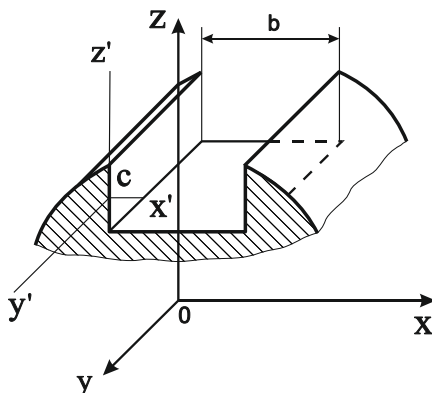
Координаты боковой поверхности шпоночного паза на валу
